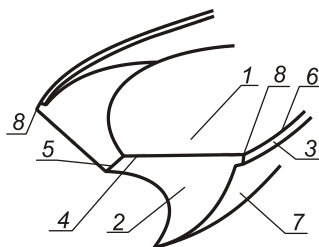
Поверхности и лезвия рабочей части винтового сверла
